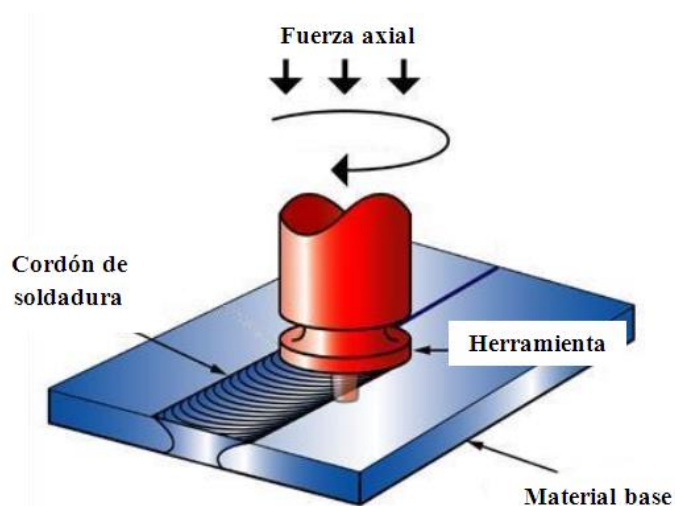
Cordón de soldadura mediante el proceso FSW
